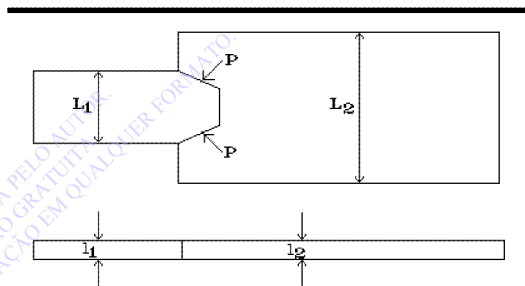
Soldagem por Centelhamento de Chapas a Topo.
